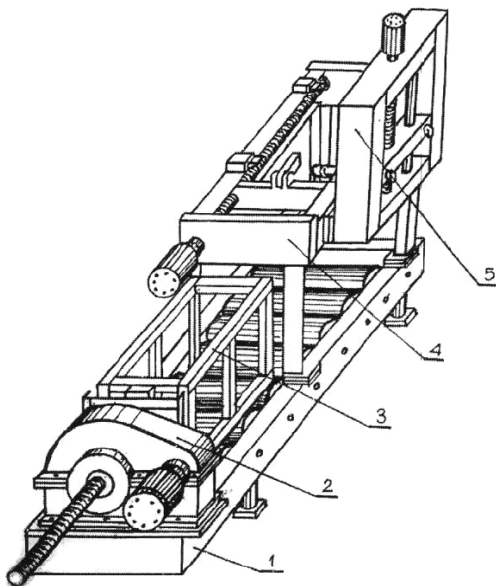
Принципова схема автоматизованого механізму подачі смуги: 1 - транспортер; 2 - привод переміщення касети; 3 - касета; 4 - механізм подачі заготовки; 5 - механізм підйому заготовки
